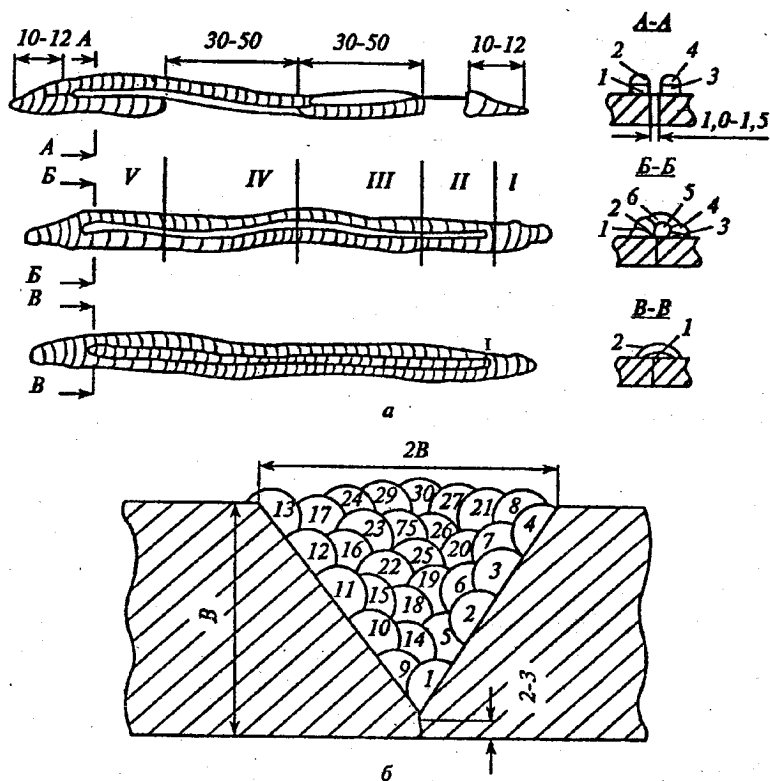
Схема наложения валиков при сварке чугуновых корпусных деталей:
